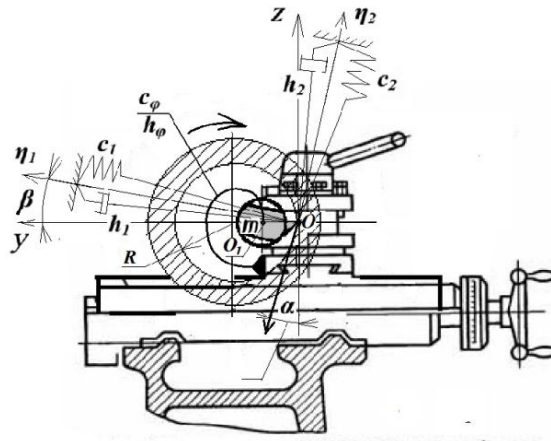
Принципова схема процесу розточування на токарному верстаті традиційної компоновки
